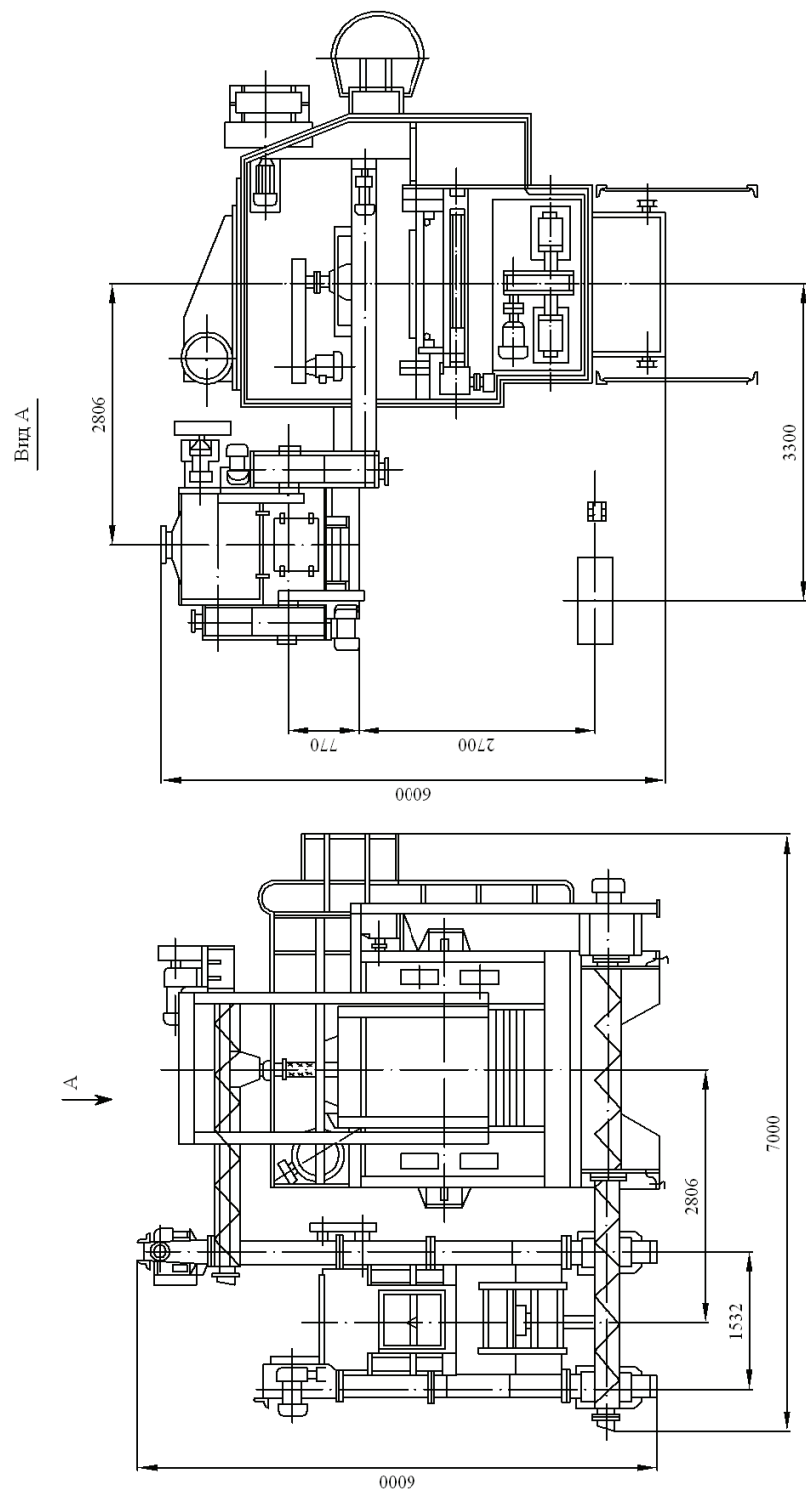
Общий вид дробемерного барабана модели 42236
